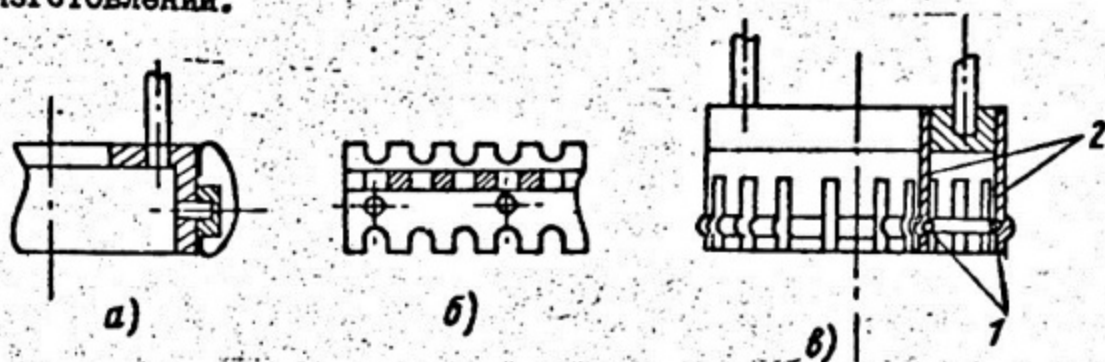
Конструкция короткозамыкающего поршня с упругими контактами
